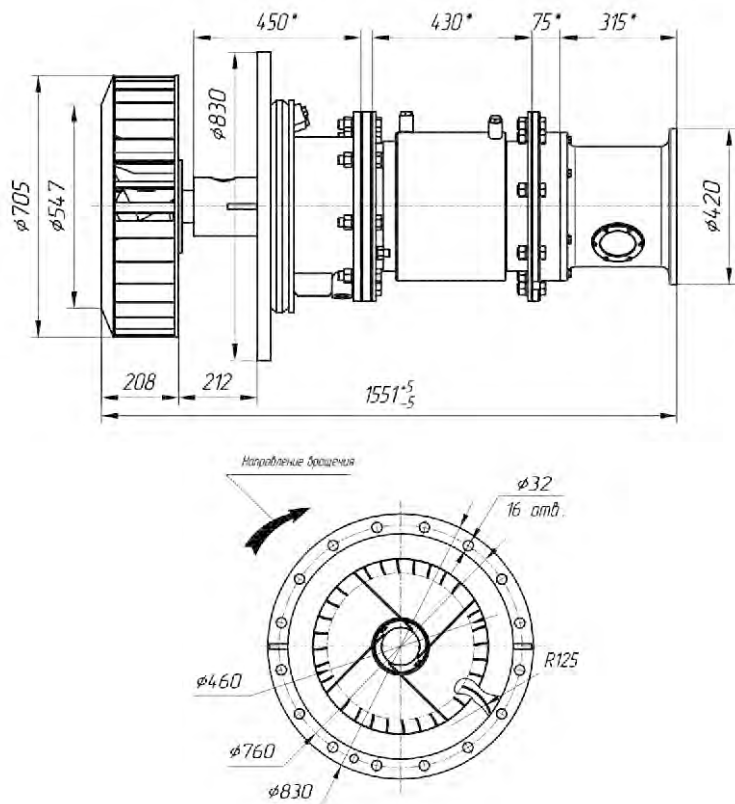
Габаритные и присоединительные размеры УЦВ 2225. (1 - Колесо рабочее; 2 - Фланец; 3 - Крышка верхняя; 4 - Вал; 5 - Ротор; 6 - Корпус статора; 7 - Статор; 8 - Крышка нижняя; 9 - Корпус охлаждения; 10 - Трубка с фланцем; а, в, д - подшипники; б, е - проверка смазки; ж, к, м - подвод воды; з, л - подвод смазки; и - отвод воды.)
